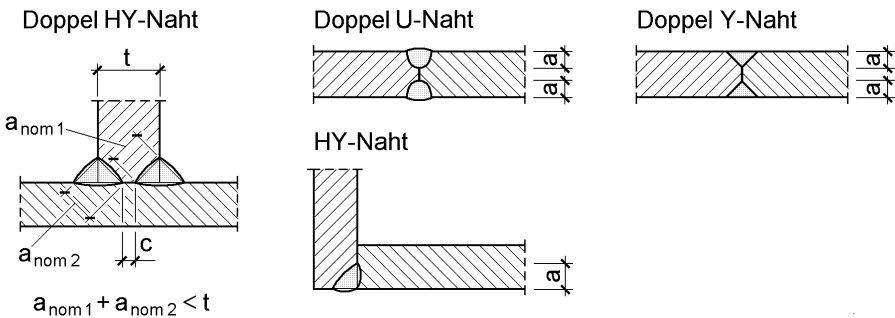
Bewertung von Anschlussdetails bezüglich der Terrassenbruchgefahr
